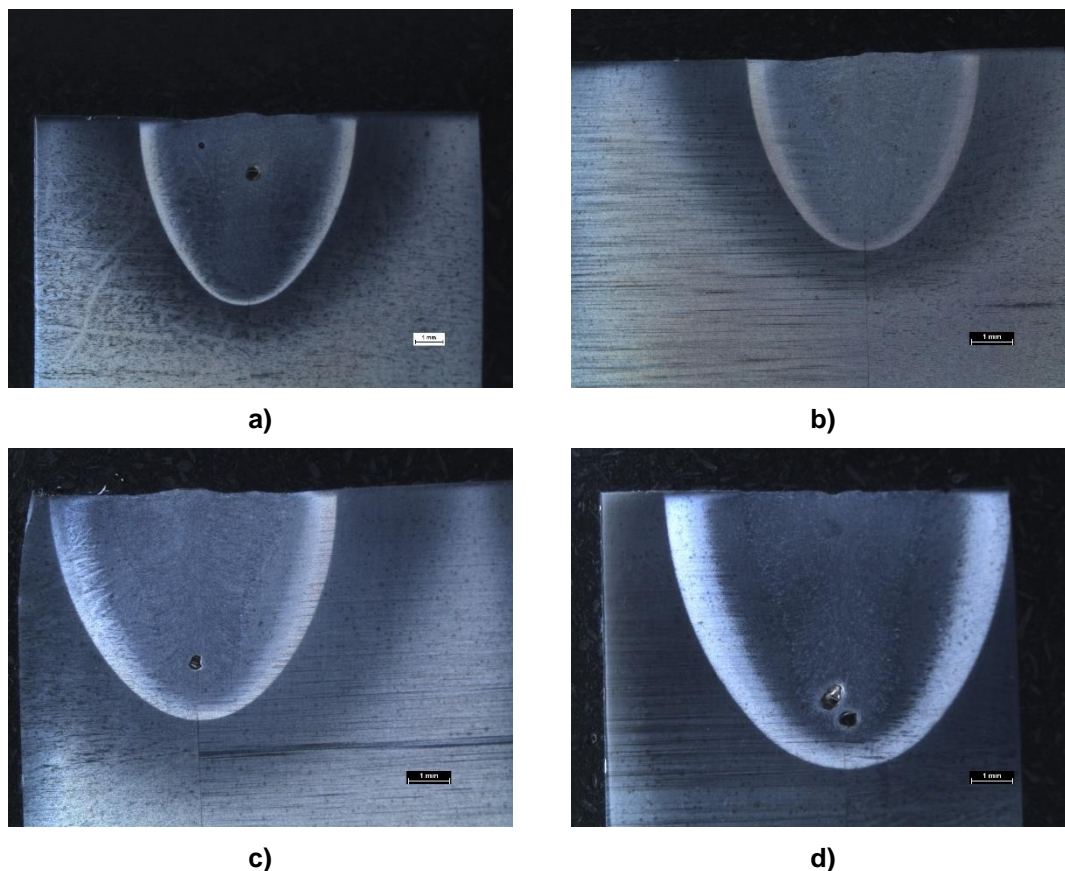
Macrografías de las uniones de acero AISI-1520 tratado térmicamente. a) Velocidad de soldadura de 10 mm/s; b) Velocidad de soldadura de 8 mm/s; c) Velocidad de soldadura de 6 mm/s; d) Velocidad de soldadura de 4 mm/s.
